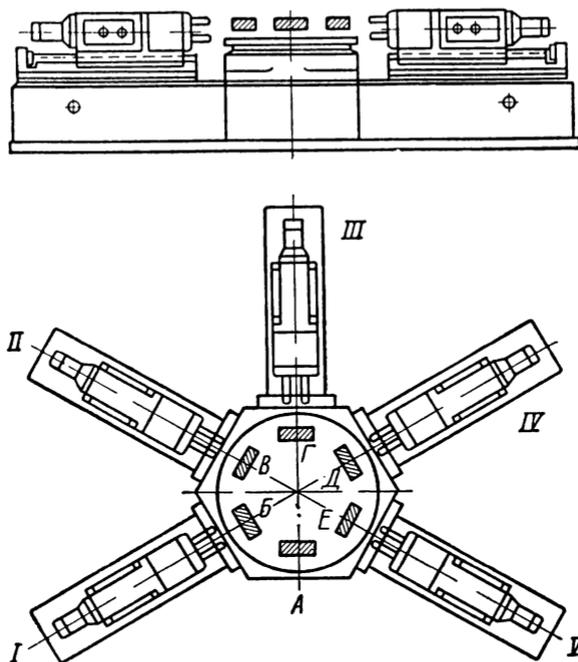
Схема агрегатного станка с пятью горизонтальными головками
